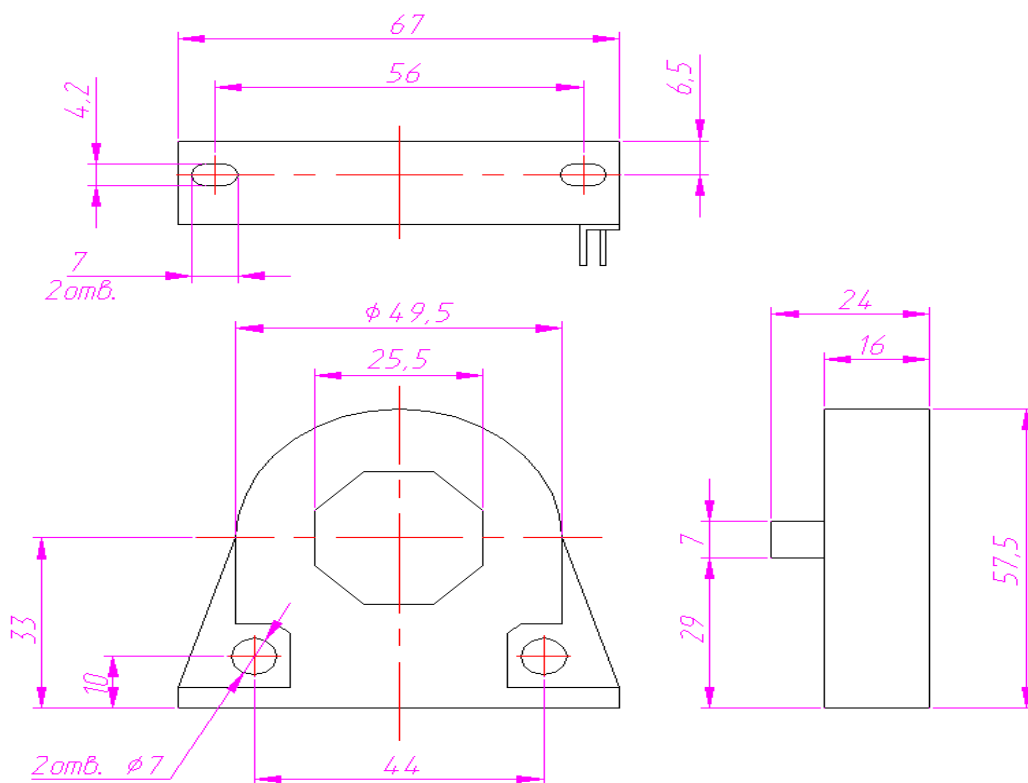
Габаритные и установочные размеры датчика тока LF 306-S.
